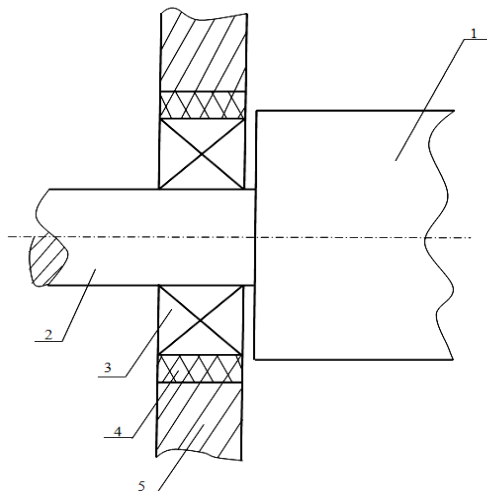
Упругая подшипниковая опора пильного цилиндра
